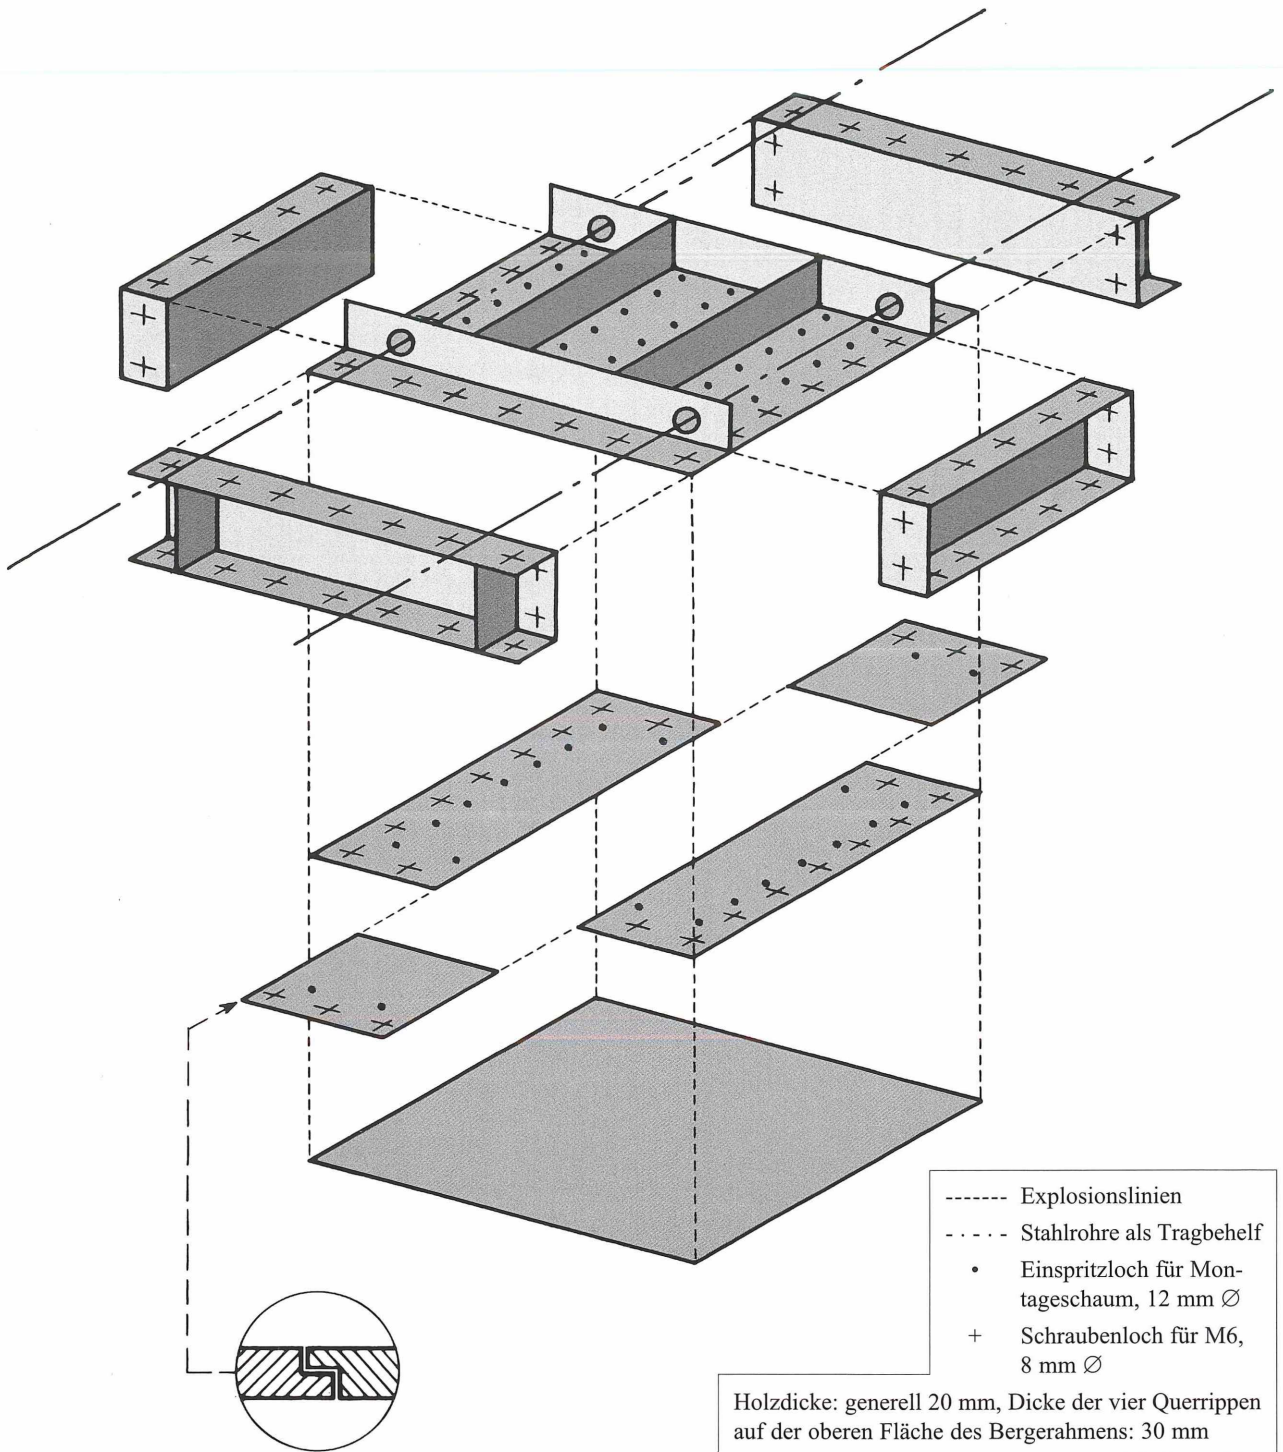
Explosionszeichnung des Bergerahmens (Zeichnung: Ing. F. Sovis)
